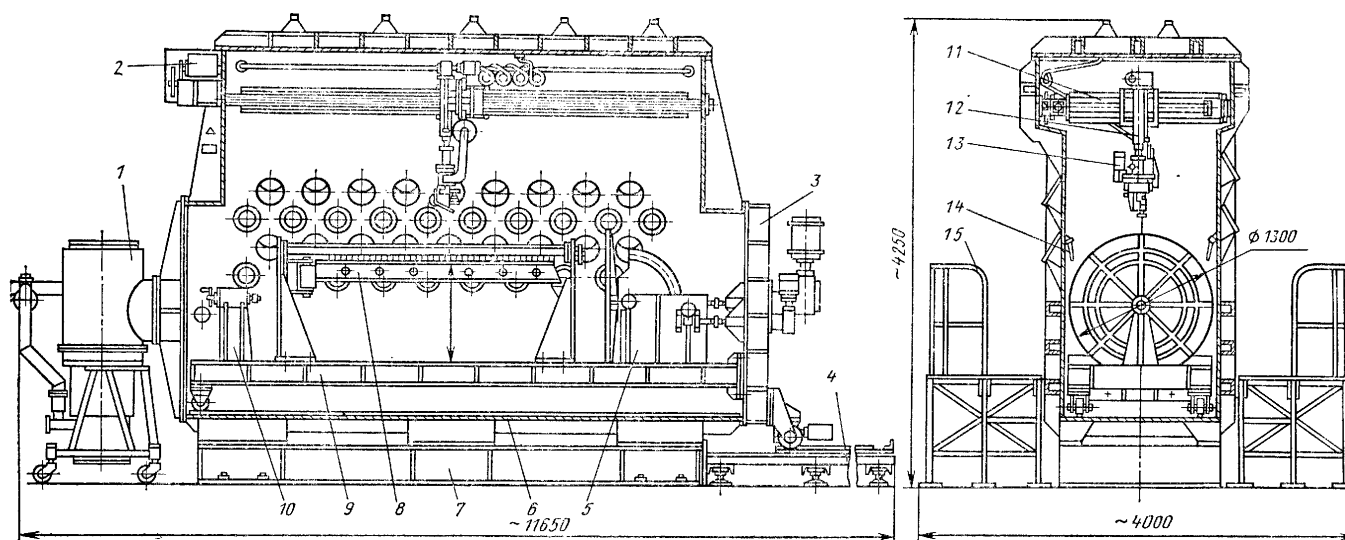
Конструктивная схема установки УСКС-7 для дуговой автоматической сварки в контролируемой атмосфере: 1 — вакуумная станция; 2 — привод сварочной горелки; 3 — откатная крышка; 4 — направляющие; 5 — манипулятор; 6 — корпус герметичной камеры; 7 — станина; 8 — устройство для сборки под сварку продольных швов обечаек; 9 — выдвижная платформа; 10 — задняя бабка; 11 — механизм поперечного и продольного перемещения сварочной головки; 12 — механизм вертикального перемещения; 13 — сварочная головка или сменная подвесная головка для приварки фланцев; 14 — ручная горелка; 15 — помост
